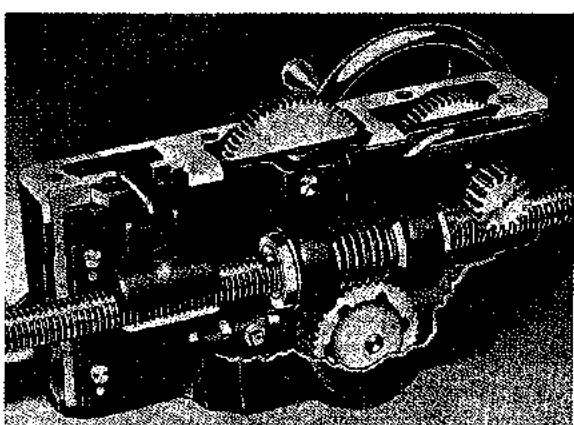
Disposición constructiva del delantal (South Bend Lathe Works).
